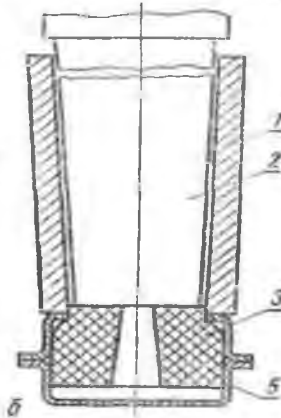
Пристосування для запресування гумової втулки карданного валу: 1 – конусна втулка; 2 – пуансон; 3 – резинова втулка; 5 – карданна головка.
